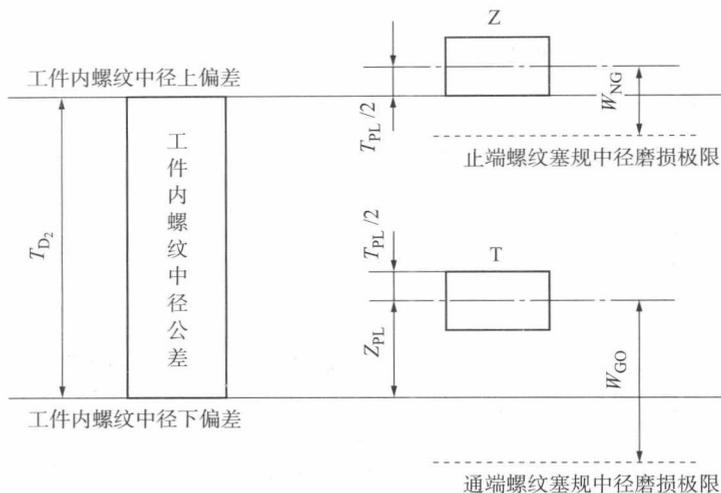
检验工件内螺纹用的螺纹塞规中径公差带
